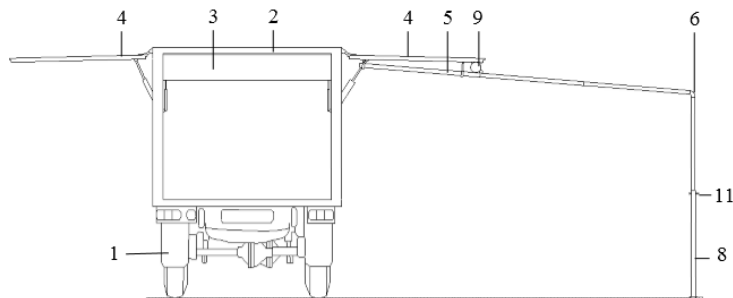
Конструкция навеса в собранном виде без укрытия его тентом:
